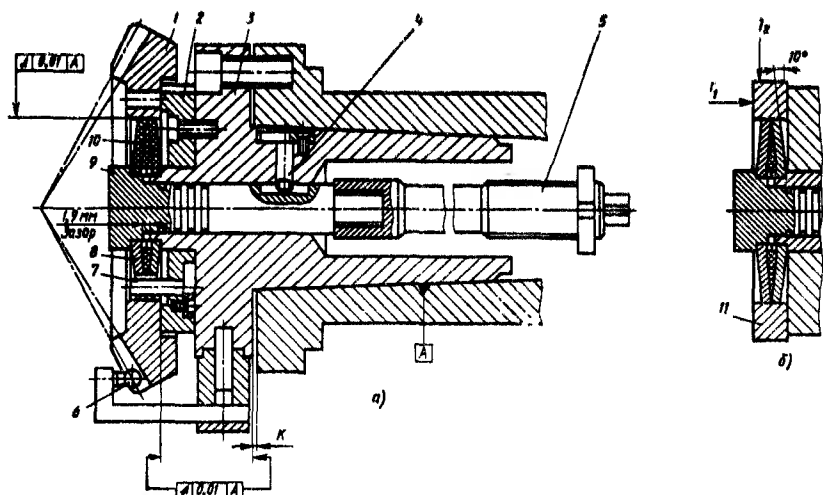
Зажимное приспособление для обработки колеса-диска:
